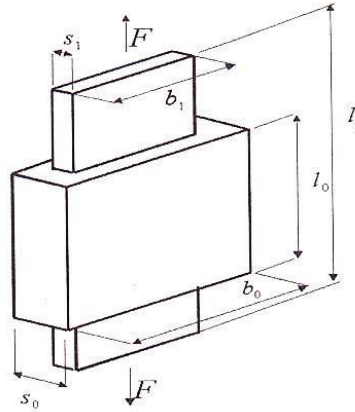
Dimensões esquemáticas em um ensaio de tração
